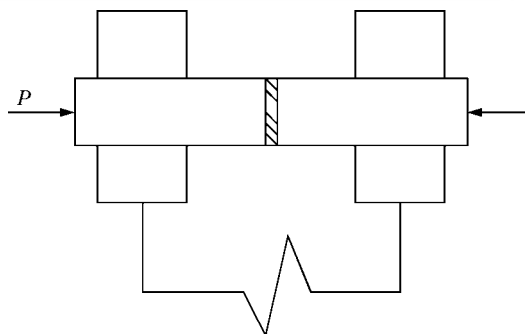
Схема контактной стыковой сварки сопротивлением интерметаллидного сплава Ti–47Al–1,5Cr–2Nb с использованием фольги (заштрихованная часть)
